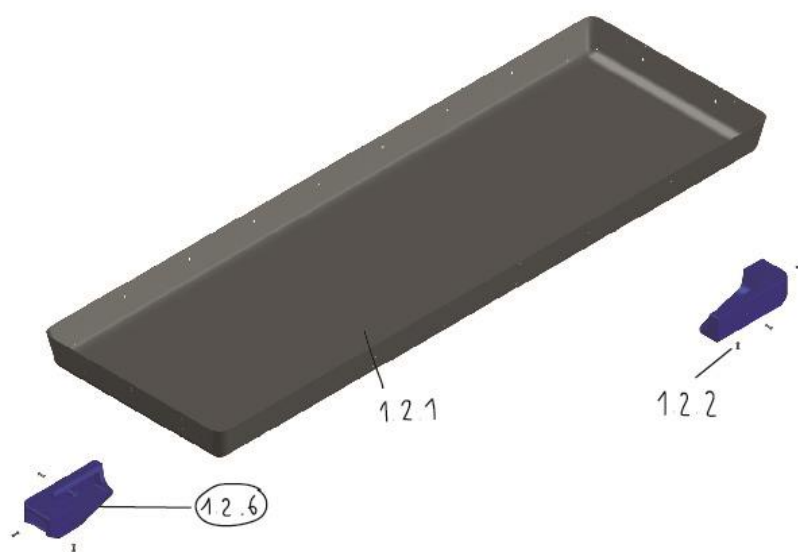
Explosionado de relaciones pieza 1.2.6
